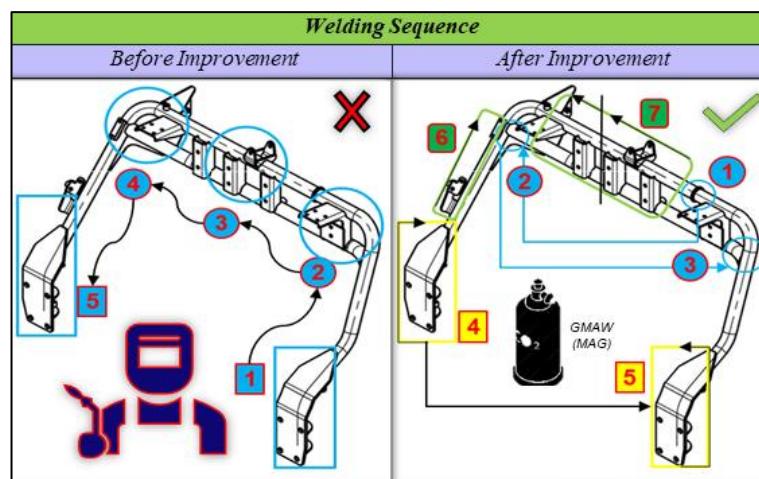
Proses *Assembly Jig Welding
